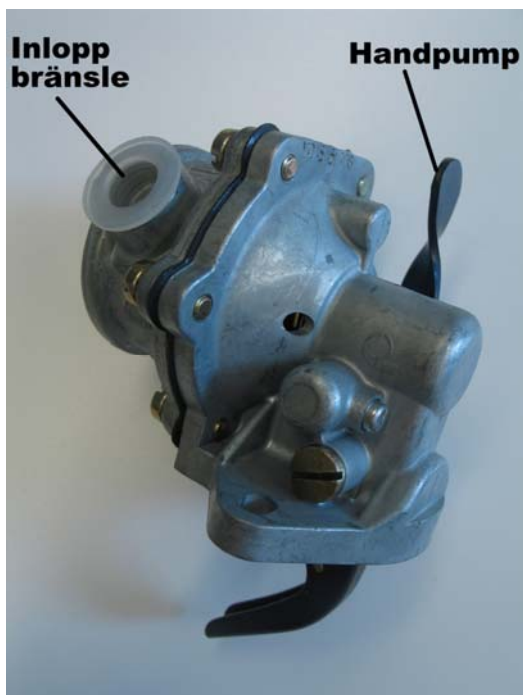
, ny matarpump (bränslepump) före montage. Vid byte ska man även sätta en ny O-ring mot motorblocket. Handpumpen används för manuell pumpning (handpump) vid luftning.
